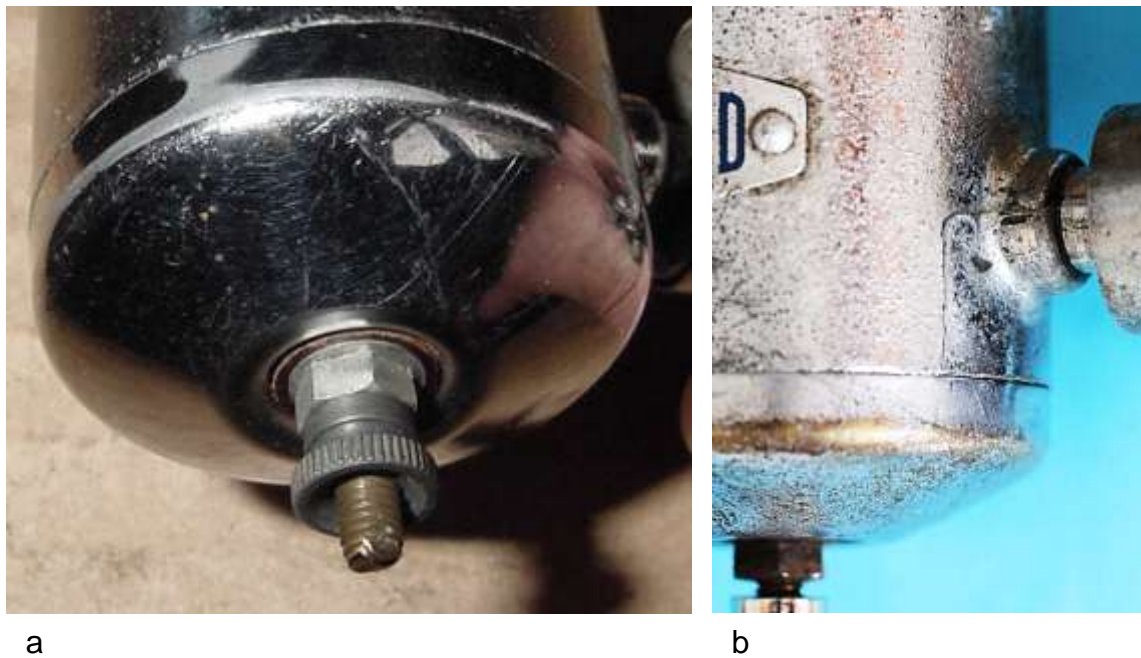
Gehäusedetails: a) Boden, b) Eingegossener Drehbolzen
